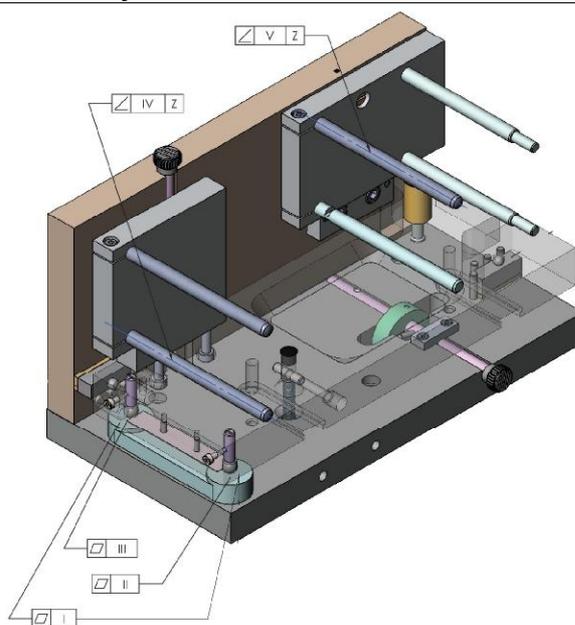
Чертеж установки для поверки систем лазерной центровки PRÜFTECHNIK CALI-CHEK T
